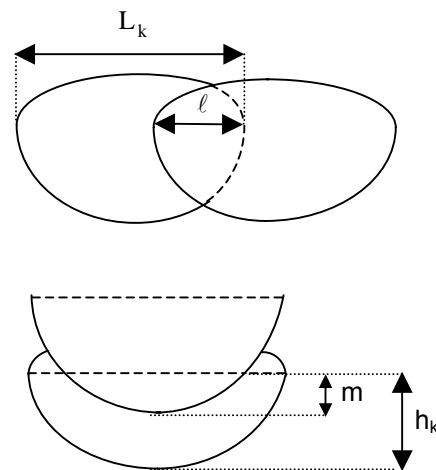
Refusions latérale R_L et verticale R_V d'une passe en soudage multi-passes.
